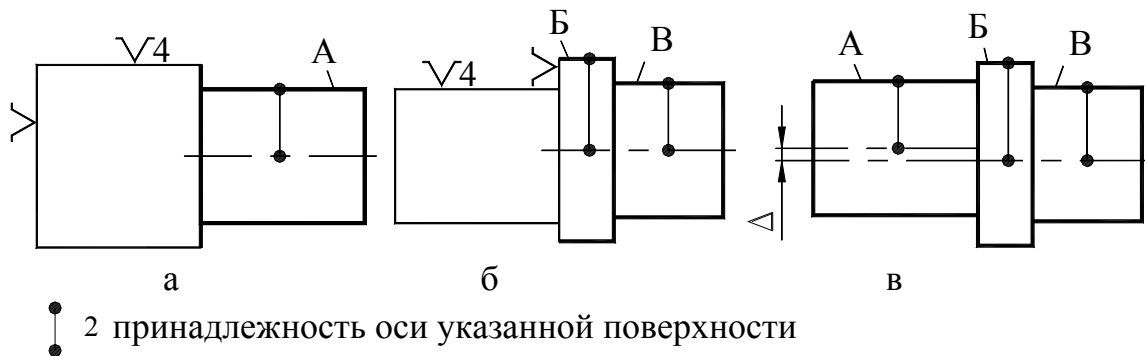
Формирование погрешности смещения осей при обработке за два установка: а, б – последовательность изготовления детали; в – эскиз полученной детали
